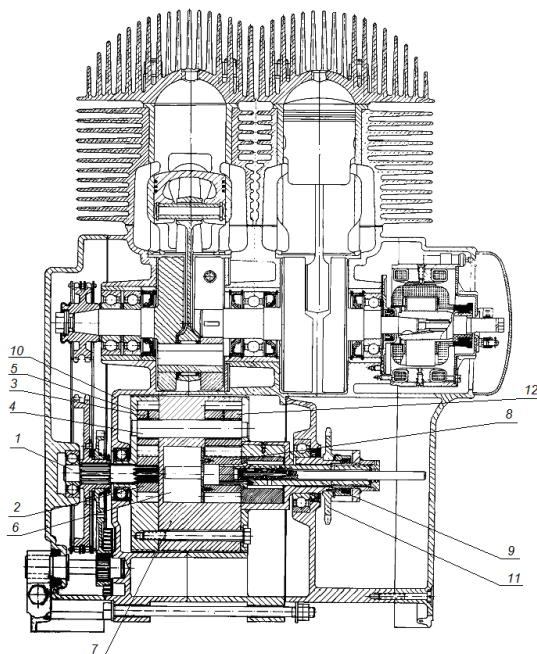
Продольный разрез двигателя мотоцикла с дифференциальной шестеренчатой гидравлической коробкой передач:
